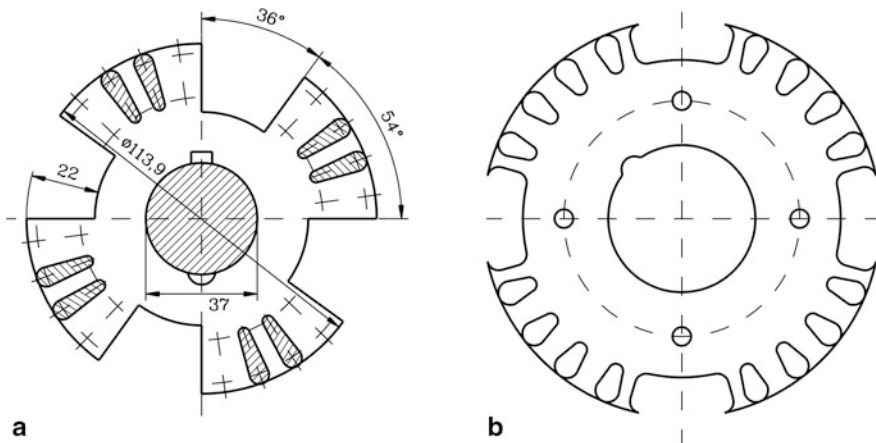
Rotorquerschnitte vierpoliger, dreisträngiger Synchron-Reluktanzmaschinen für 50 Hz, 1500/min, Oberflächenkühlung mit Gehäusekühlrippen und Wellenlüfter, Isolierstoffe des Stators mit Wärmeklasse F, (a) 2.2 kW, Achshöhe 112 mm, ausgefräste Pollücken, Käfig-Gittersegmente je Pol (Quelle: Binder 1989), (b) 550 W, Achshöhe 80 mm, ausgestanzte Pollücken, Aluminium-Druckgusskäfig füllt auch die Pollücken aus, durchgängige Kurzschlussringe. (Quelle: Siemens AG), (Maßstäbe bei a) und b) unterschiedlich!)
